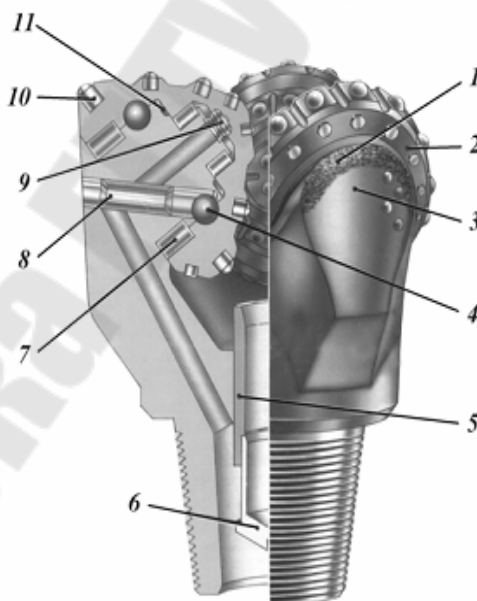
Конструкция долота для бурения с продувкой воздухом: 1 – наплавка твердым сплавом; 2 – шарошка; 3 – лапа; 4 – шарикоподшипник; 5 – сопло; 6 – клапан; 7 – роликоподшипник; 8 – замок; 9 – подпятник; 10 – твердосплавной зубок; 11 – упорный подшипник скольжения
